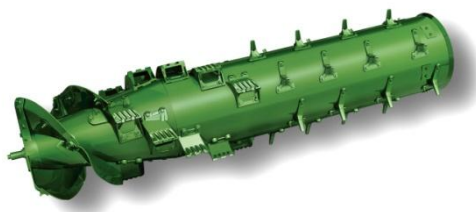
Общий вид ротора зерноуборочного комбайна S660
